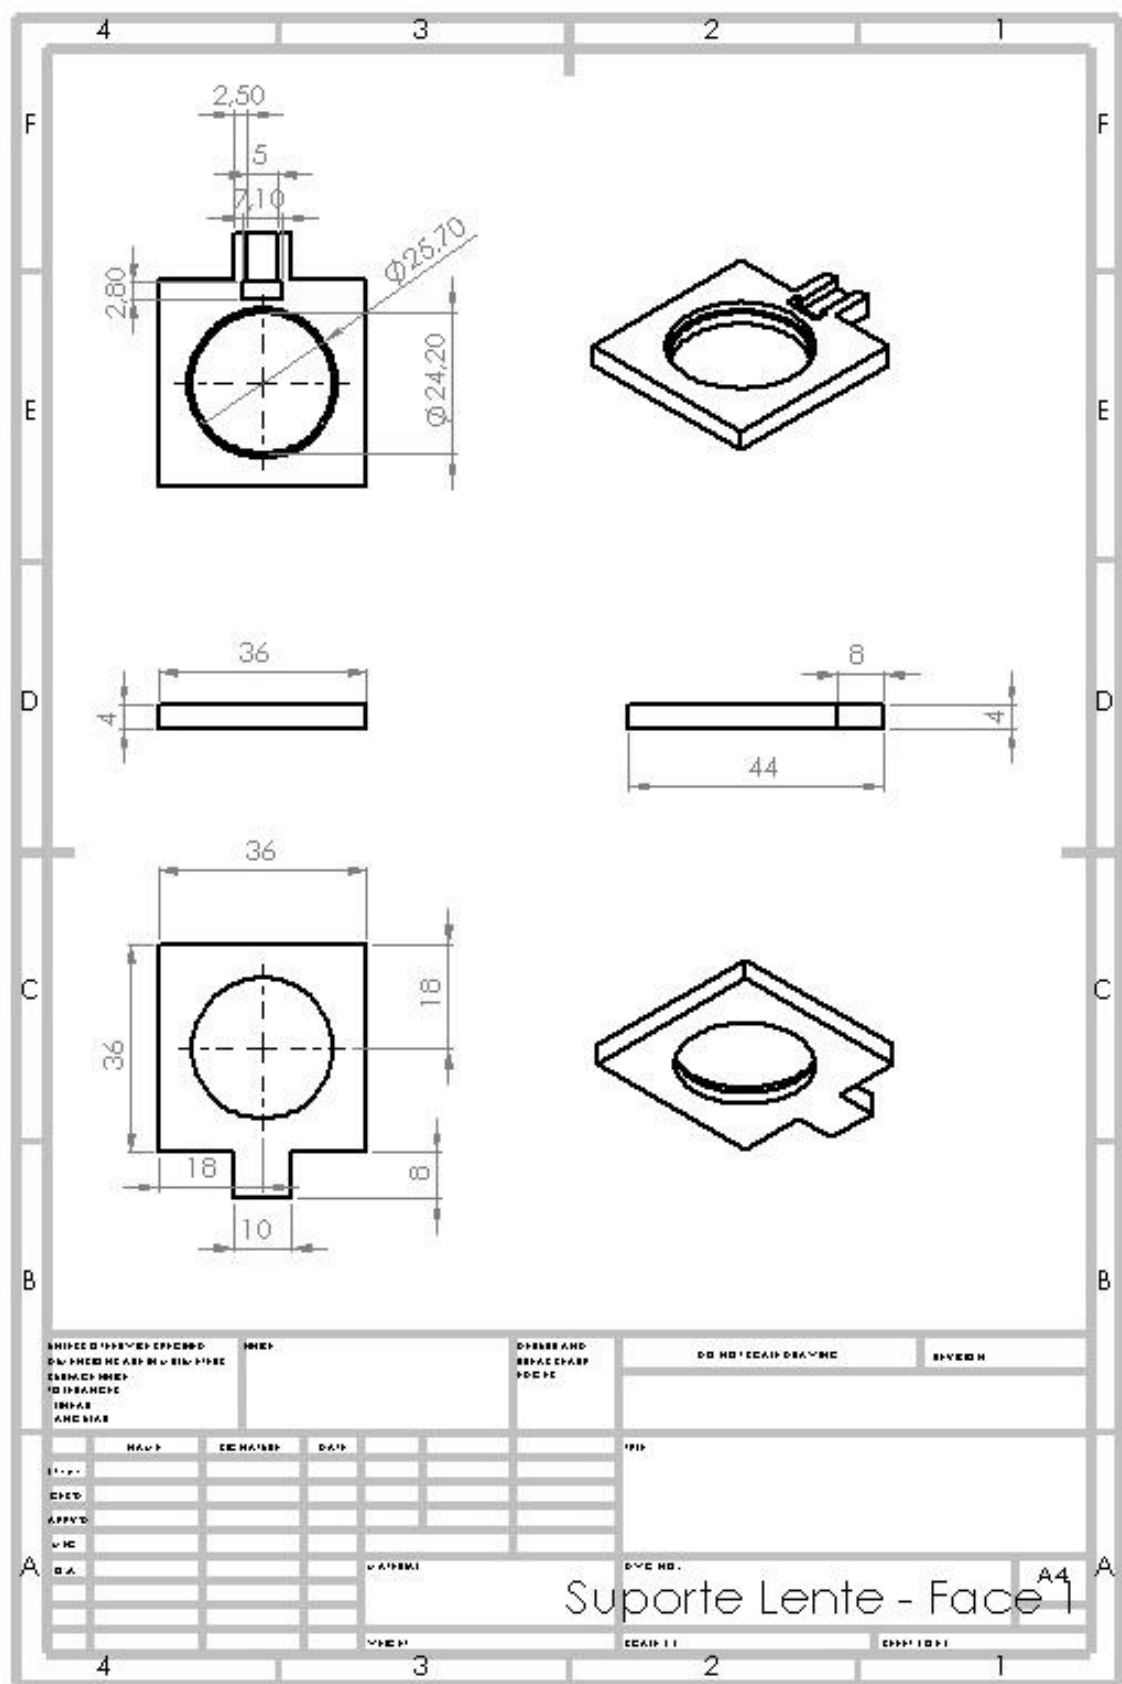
Desenho técnico da peça Suporte Lente - Face 1
